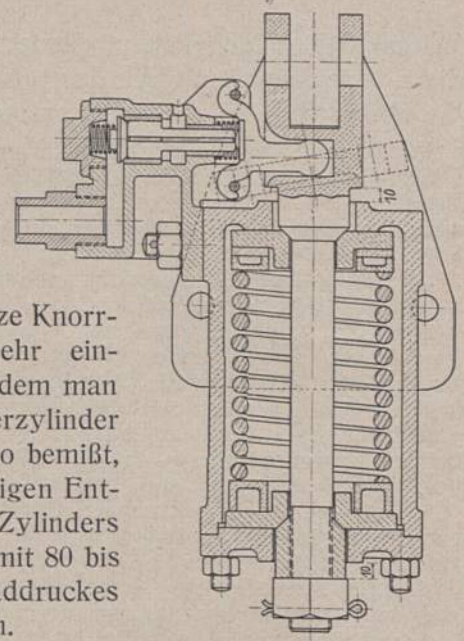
zeigt die Bauform des Bremsdruckreglers.
